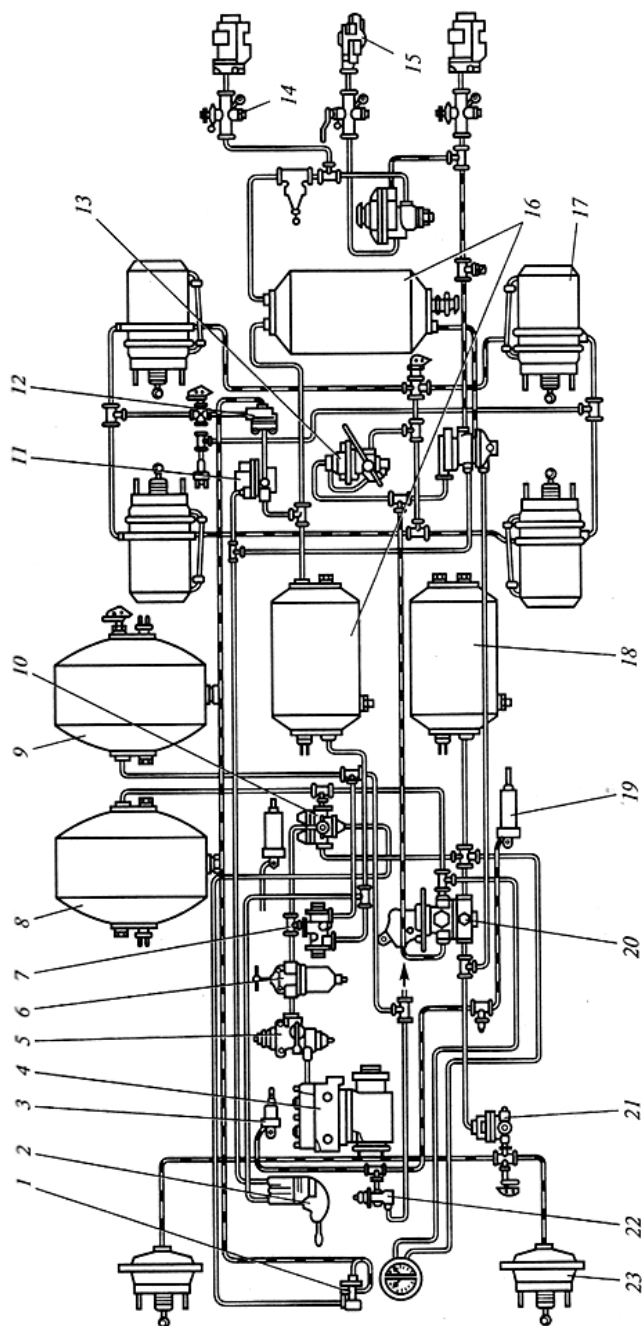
Пневматический тормозной привод грузового автомобиля: 1, 2, 14, 20, 22 — краны; 3, 19 — цилиндры; 4 — компрессор; 5, 13 — регулятор; 6 — предохранители; 7, 10, 11, 12, 21 — клапаны; 8, 9, 16, 18 — баллоны (ресиверы); 15 — головка подсоединения прицепа; 17, 23 — тормозные камер
